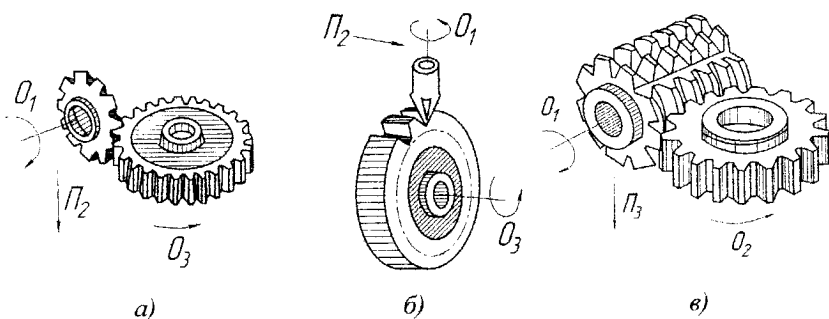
Формоутворення зубців циліндричних коліс за допомогою фрез: а) – дискової, б) – пальцевої, в) – черв'ячної
